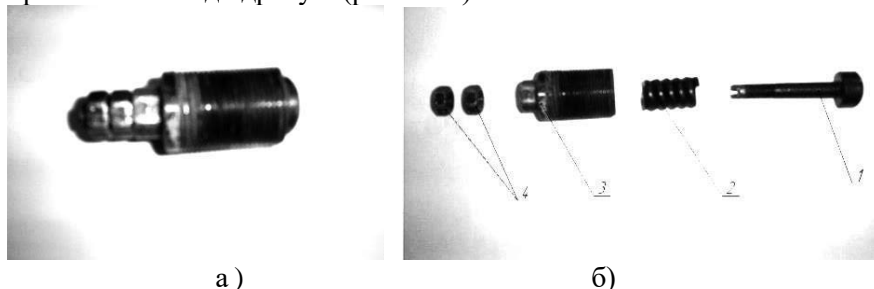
Механізм, який створює зусилля притискання роликів до дроту: а – у зборі; б – складові деталі; 1 – шток; 2 – пружина; 3 – корпус; 4 – гайки
